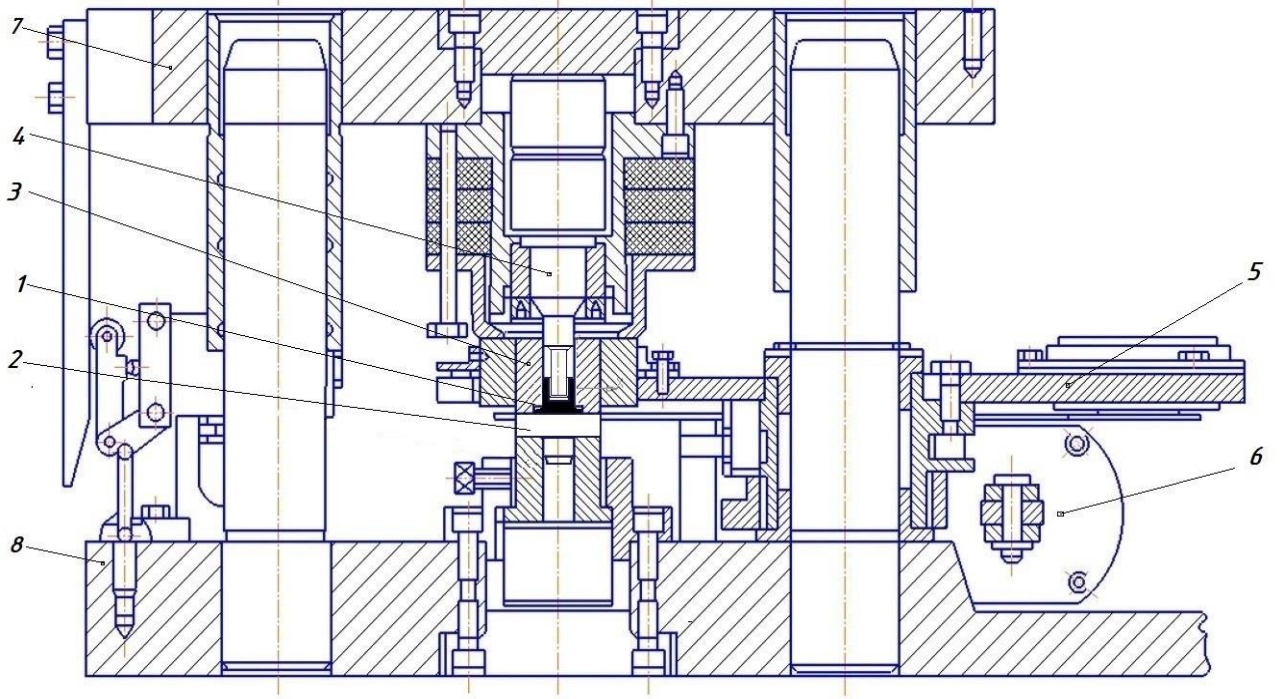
Штамп для виготовлення деталі типу стакан з фланцем з револьверною подачею
